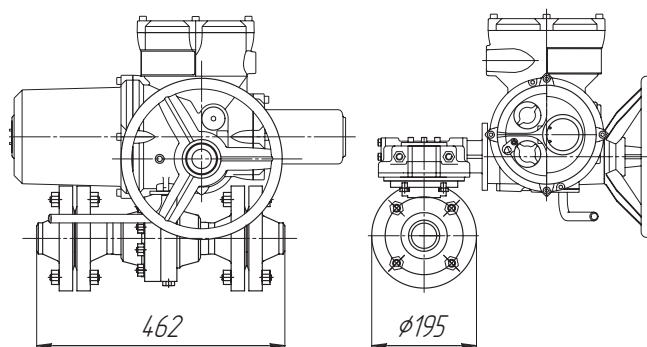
Кран шаровой надземный с электроприводом и фланцевым соединением
